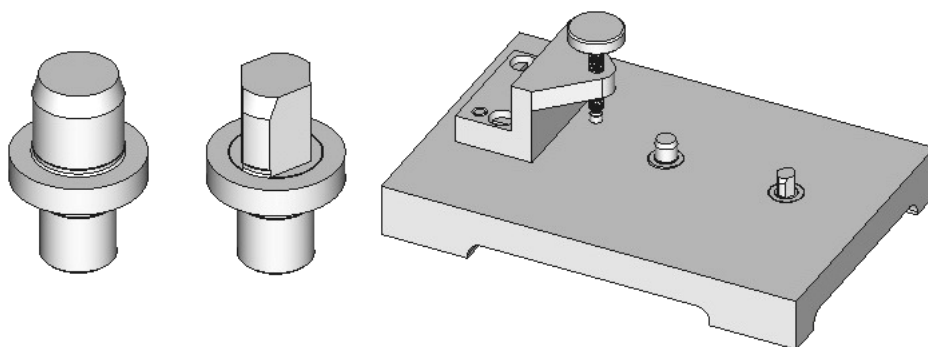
Пальцы цилиндрический полный и цилиндрический срезанный
